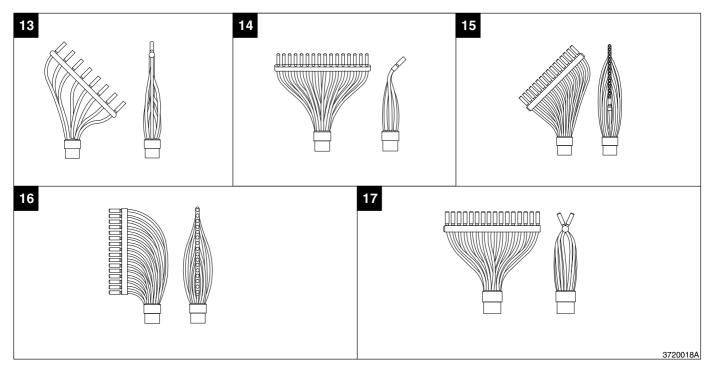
Sprühköpfe (Zeichnungen nicht maßstabsgetreu)
